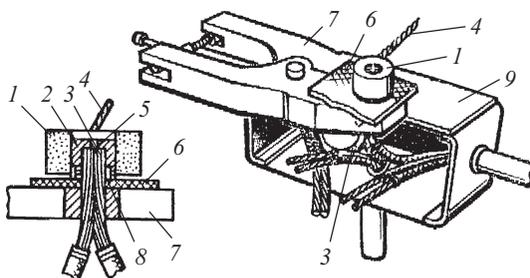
Сварка алюминиевых проводов термитными патронами:
